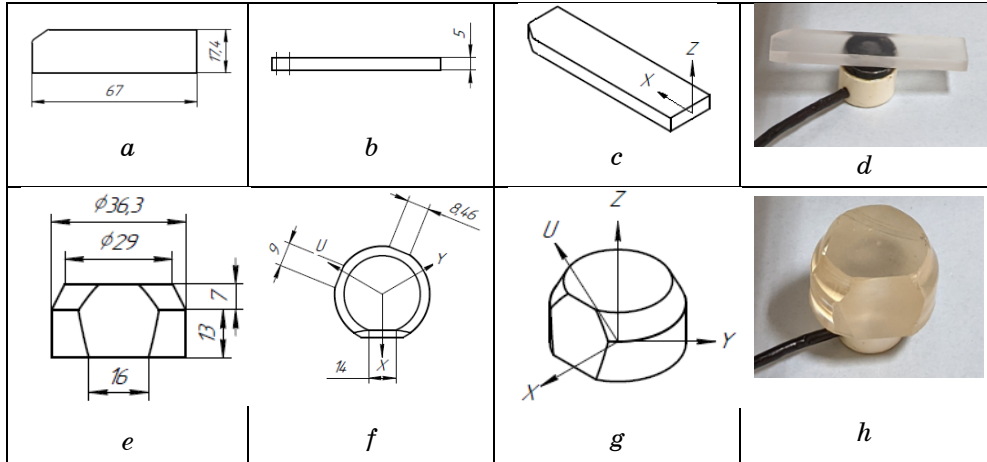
Кристалл ниобата лития. Обработанный в виде пластины: a — вид сверху; b — вид спереди; c — 3D-вид; d — фотография.
